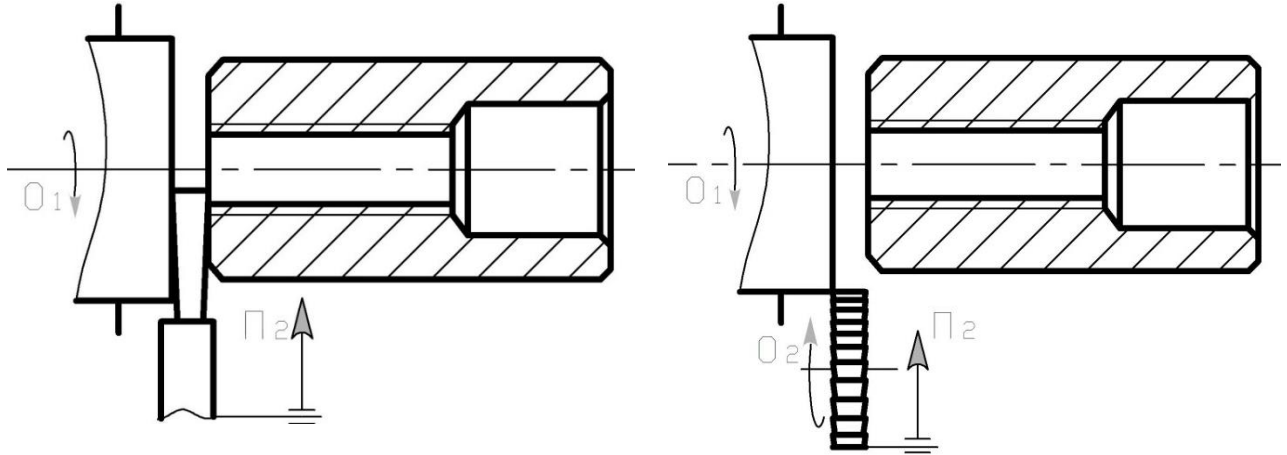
Відрізання деталі різцем Рисунок 2.7 - Відрізання деталі фрезою
